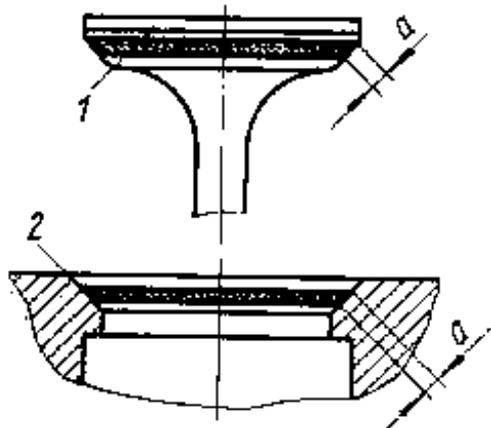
Притертые поверхности клапана и седла: 1- поверхность клапана; 2-поверхность седла
